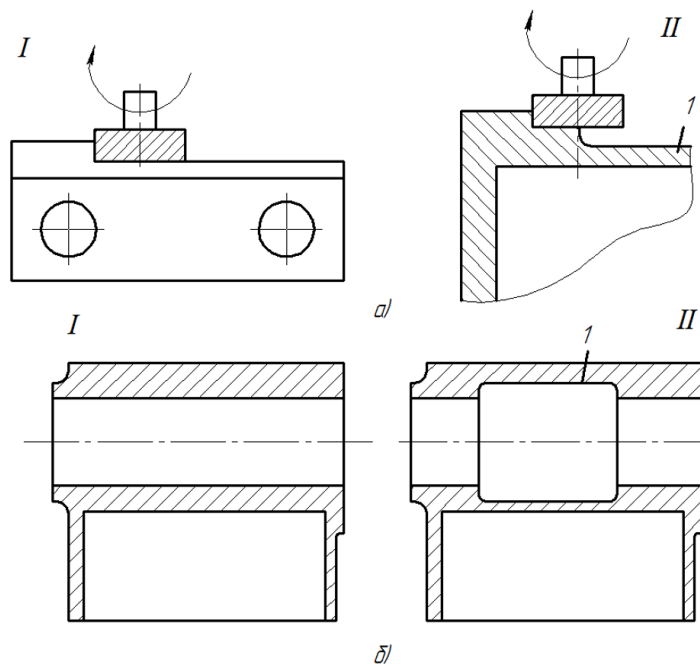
Скорочення довжини оброблюваних поверхонь
